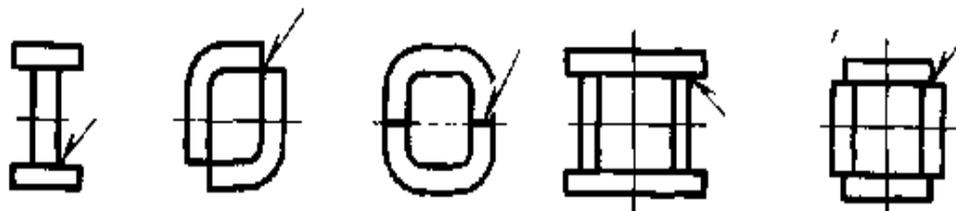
Элементы конструкции с симметричным расположением деталей и швов
